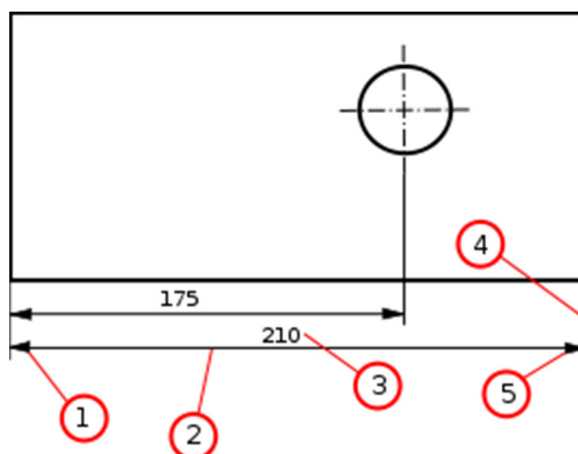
Componentes de cotas: (1) marca inicial (2) línea de cota (3) cifra de cota (4) línea auxiliar de referencia (5) marca final.
